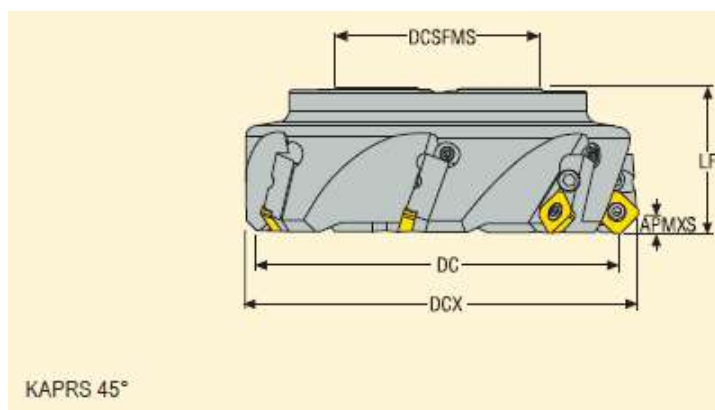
Фреза для фрезерования торца на валу К-12-11
